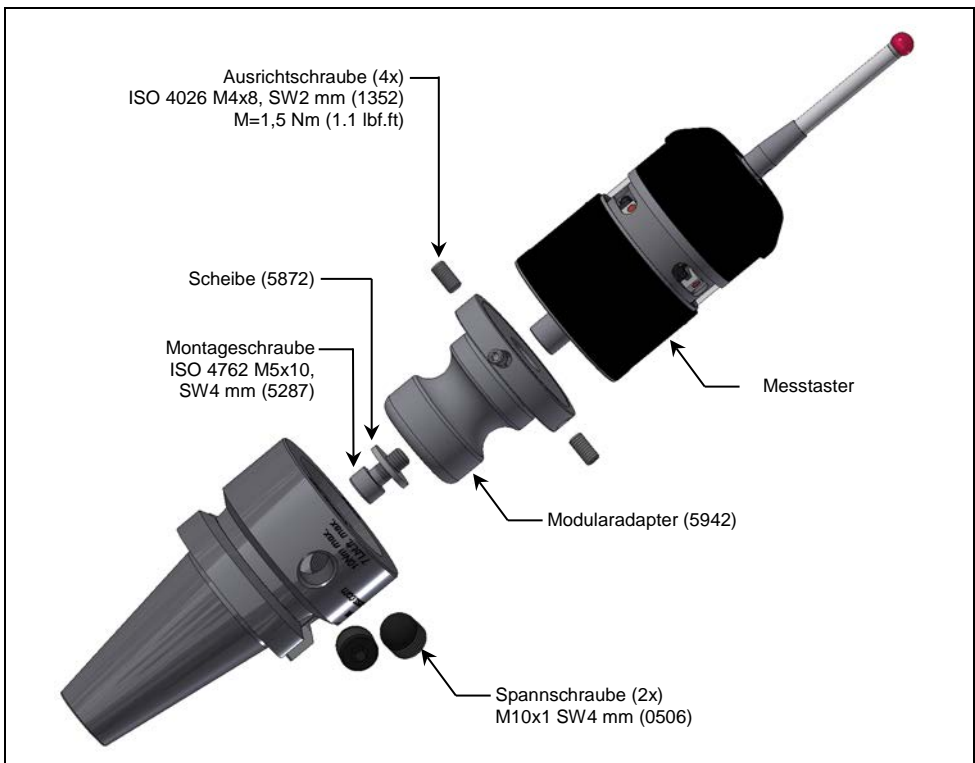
Montage/Demontage der Werkzeugaufnahme
